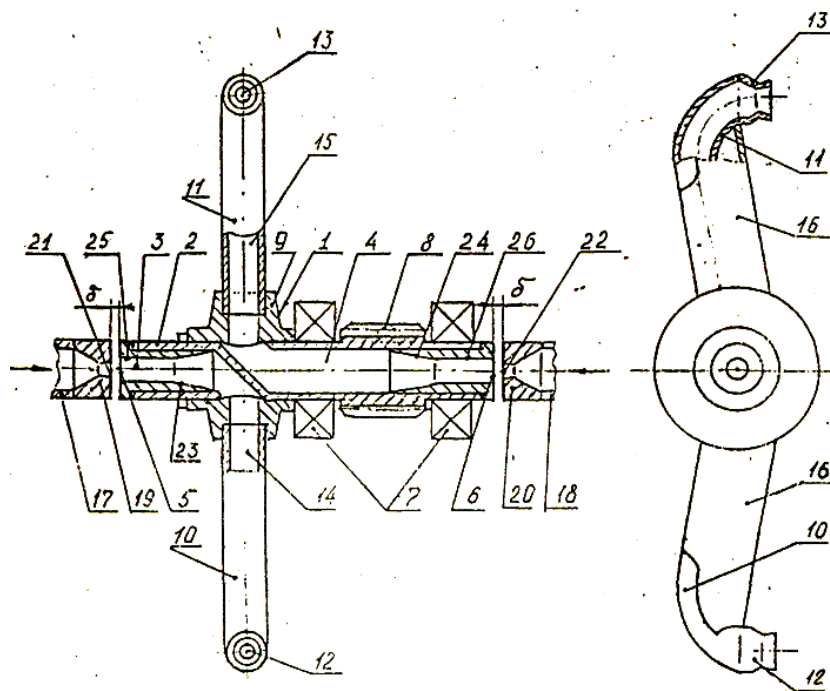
Конструктивна схема реверсивної струминно-реактивної турбіни.
